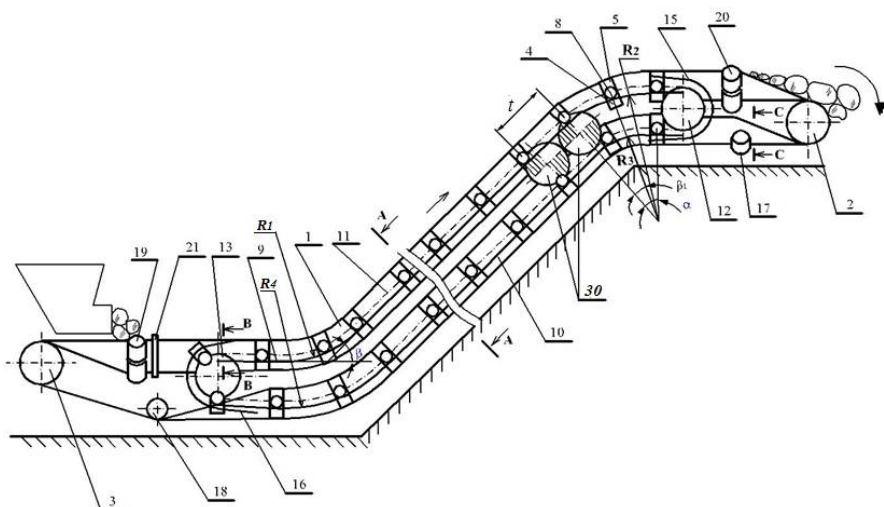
Крутонаклонный ленточно-колесный конвейер для крупнокусковых грузов, схема конвейера
